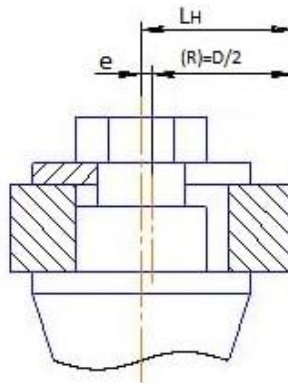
Визначення похибки базування під час базування заготовки по циліндричному отвору
